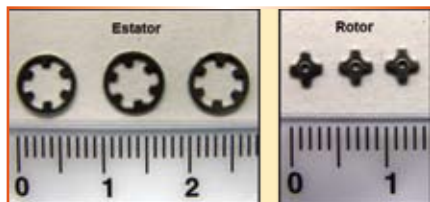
Rotor e estator obtidos pelo processo de corte convencional
